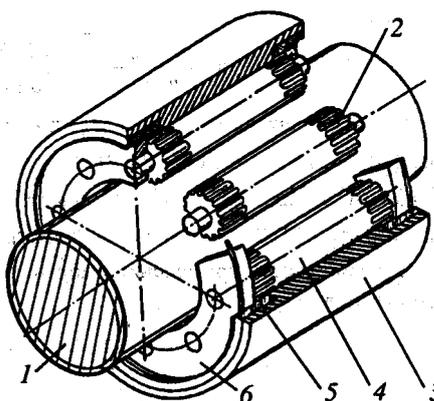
Общий вид планетарной роликовинтовой передачи (ПРВП)
